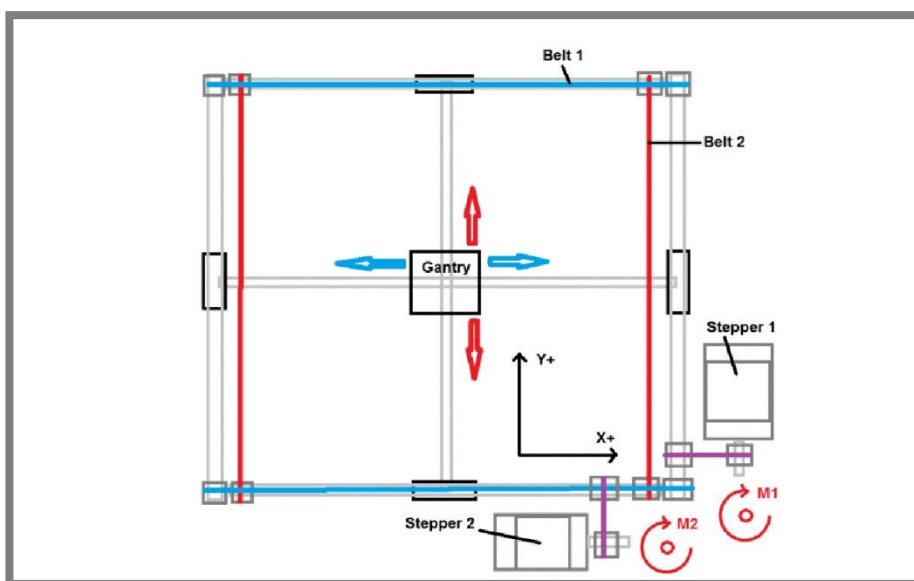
Schematické zobrazení mechanismu Hbot [22]
